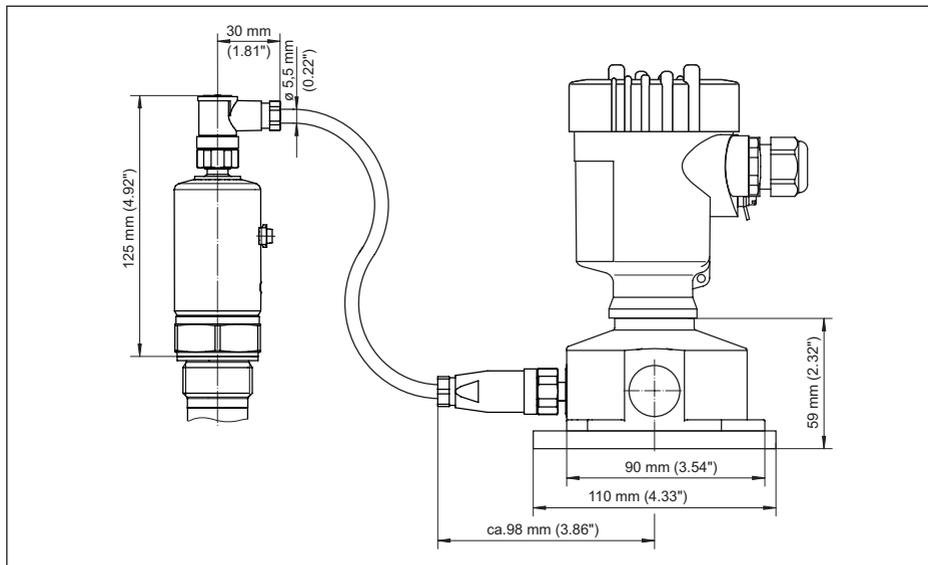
Caixa do sensor e caixa rebaixada (caixa do aparelho)
